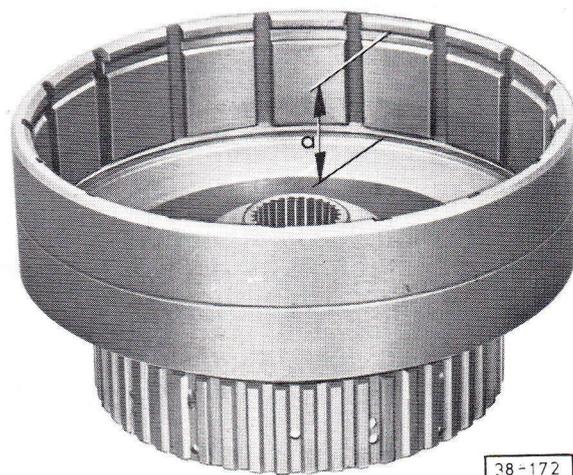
Mesure de la position de la gorge pour segment d'arrêt
